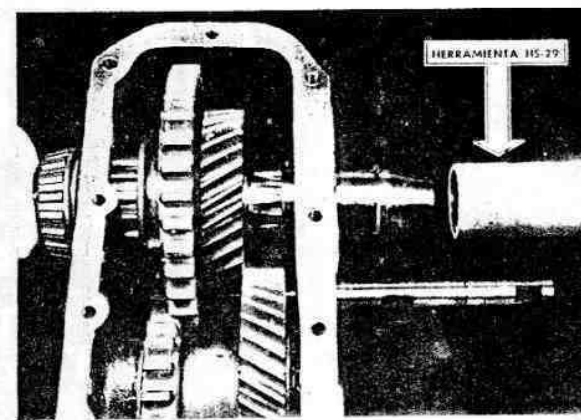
Instalando el aro retén del engranaje del eje principal, con la herramienta H5-29.
